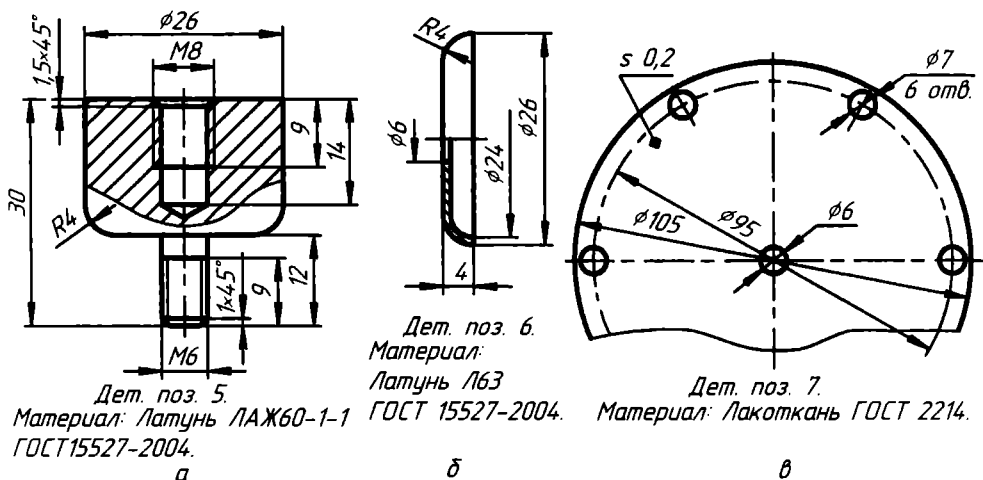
Чертежи: а — наконечника; б — шайбы; в — мембраны
